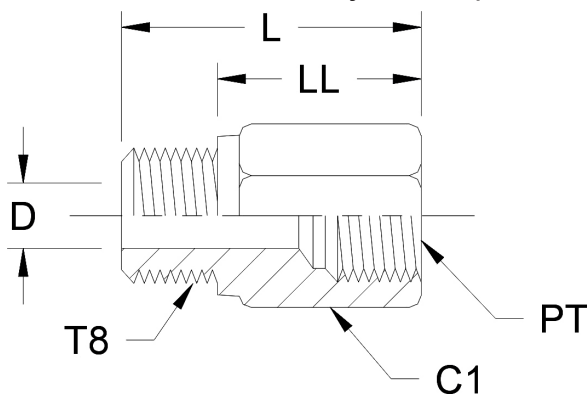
adaptateur de conversion - métrique à NPTF - dessin dimensionnel
